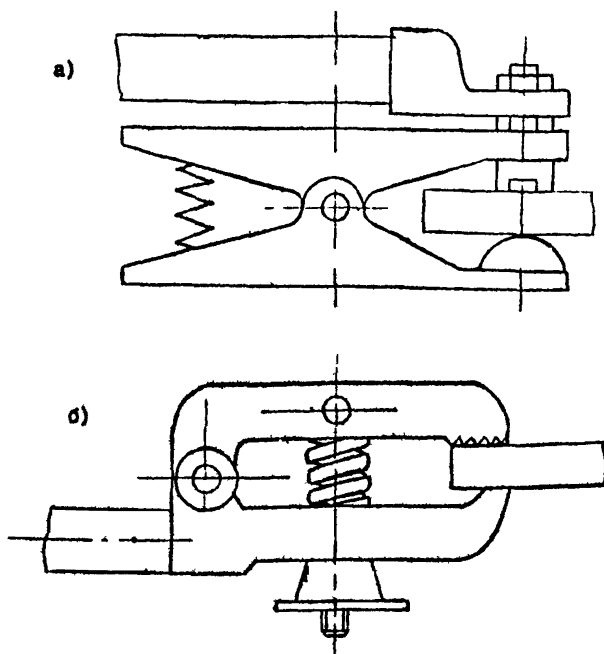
Зажимы для присоединения сварочного провода к свариваемому изделию:
